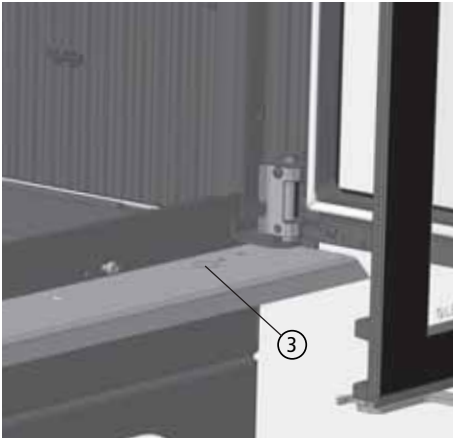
vorgelaserte Bohrung für Türschalter in unterer Blende ausbrechen bei KALA ES 45 oder KALA ES 55
